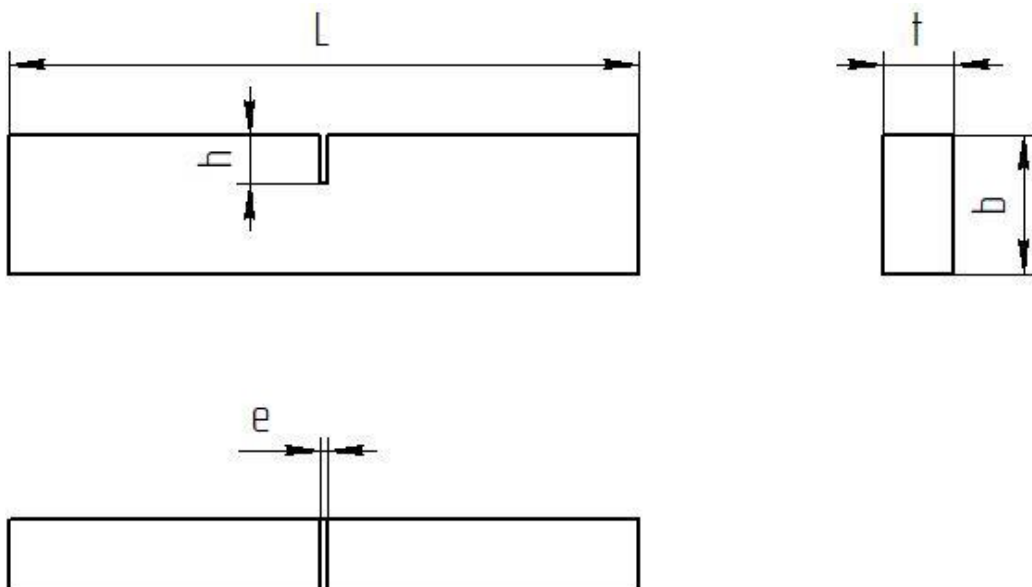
Чертеж образца для прочностных испытаний по трехточечной схеме нагрузки
